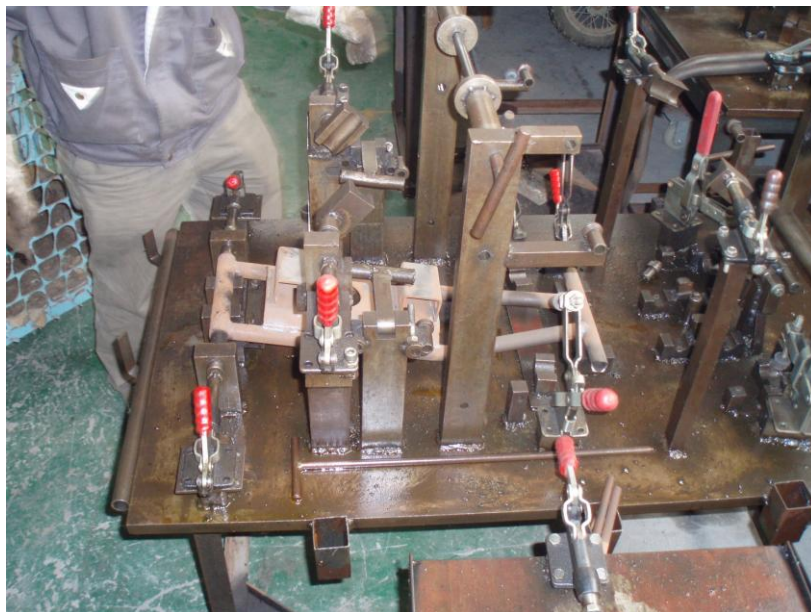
MOLDE Y COMPONENTES TUBULARES
